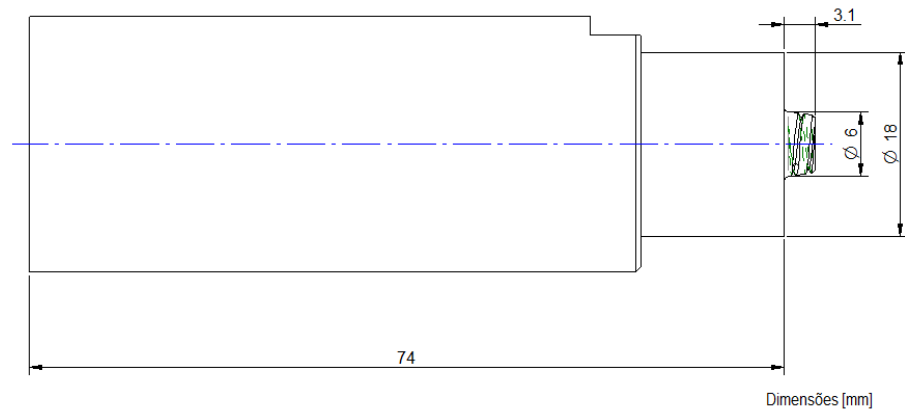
Ferramenta para soldagem FSW e detalhes do ombro e pino.
